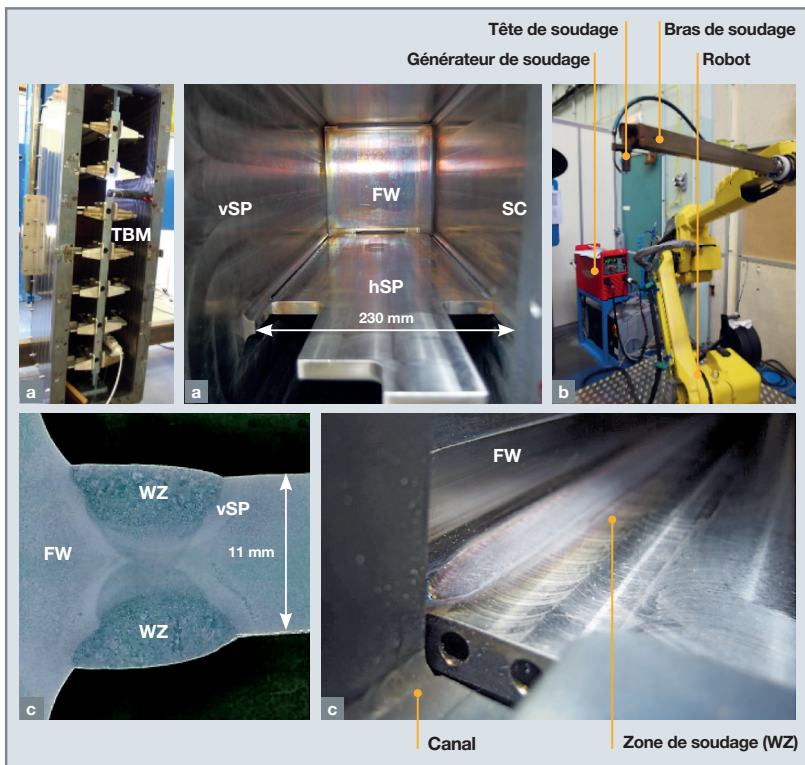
(a) Positionnement, ajustement et soudage des plaques vSP et hSP dans la Box, (b) équipement de soudage TIG robotisé et (c) inspection visuelle de la soudure (face endroit et sur coupe transversale).
